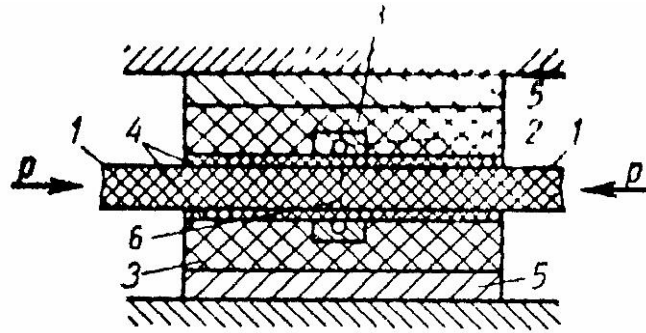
Схема контактної-теплової зварювання встик пресуванням: 1 – матеріал, що зварюється; 2 - нагрівач; 3 — теплоізоляція; 4 - прокладка; 5 - металева пластина; 6 - зварний шов
